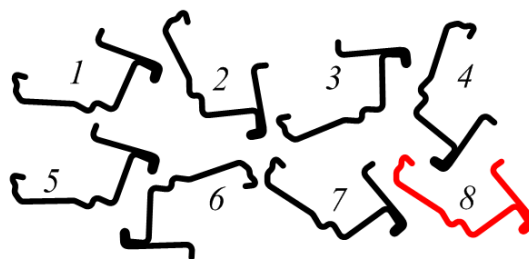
Варианты расположения сечения профиля «косяк» чертеже или в чистовой клети станка
